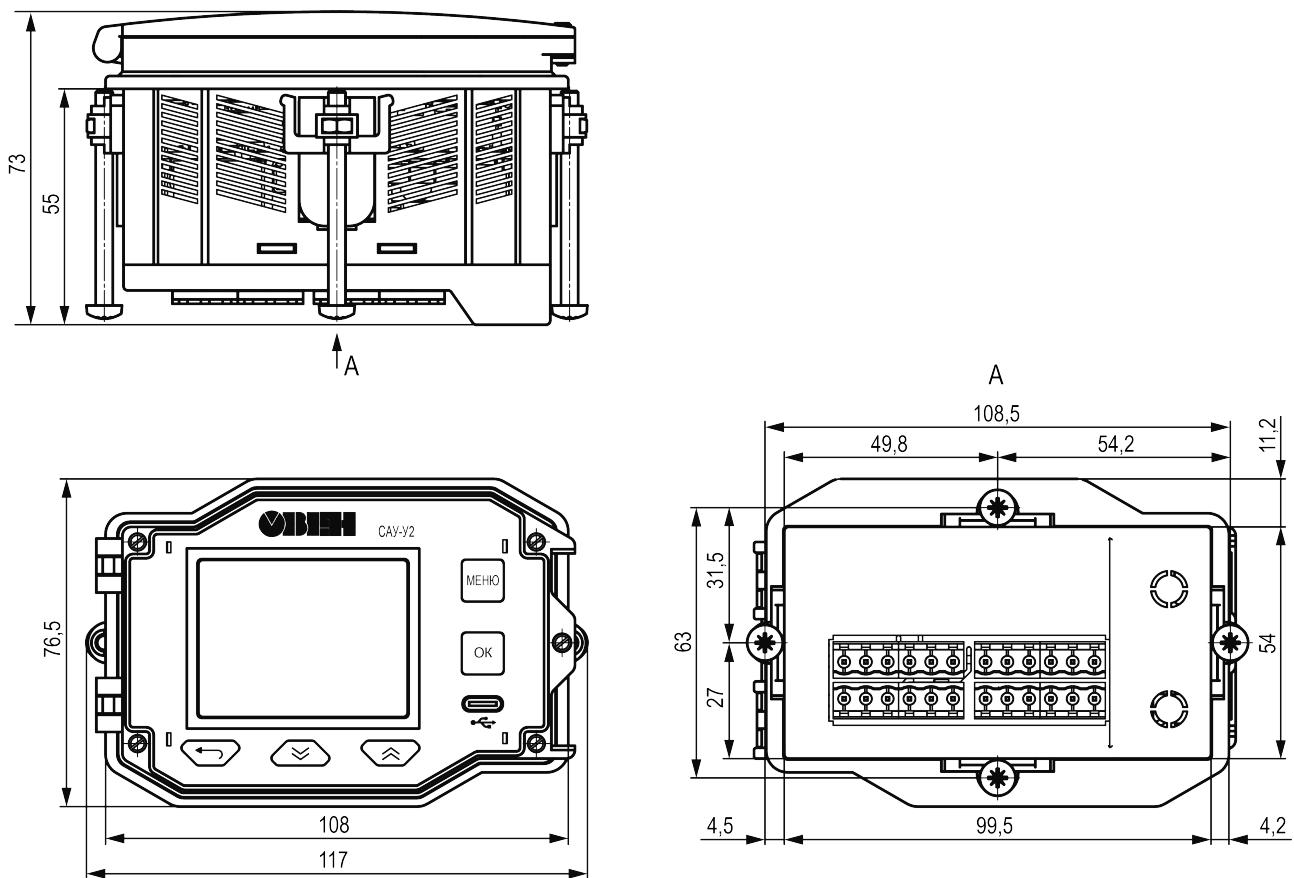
Габаритные и присоединительные размеры САУ-У2-Щ12
